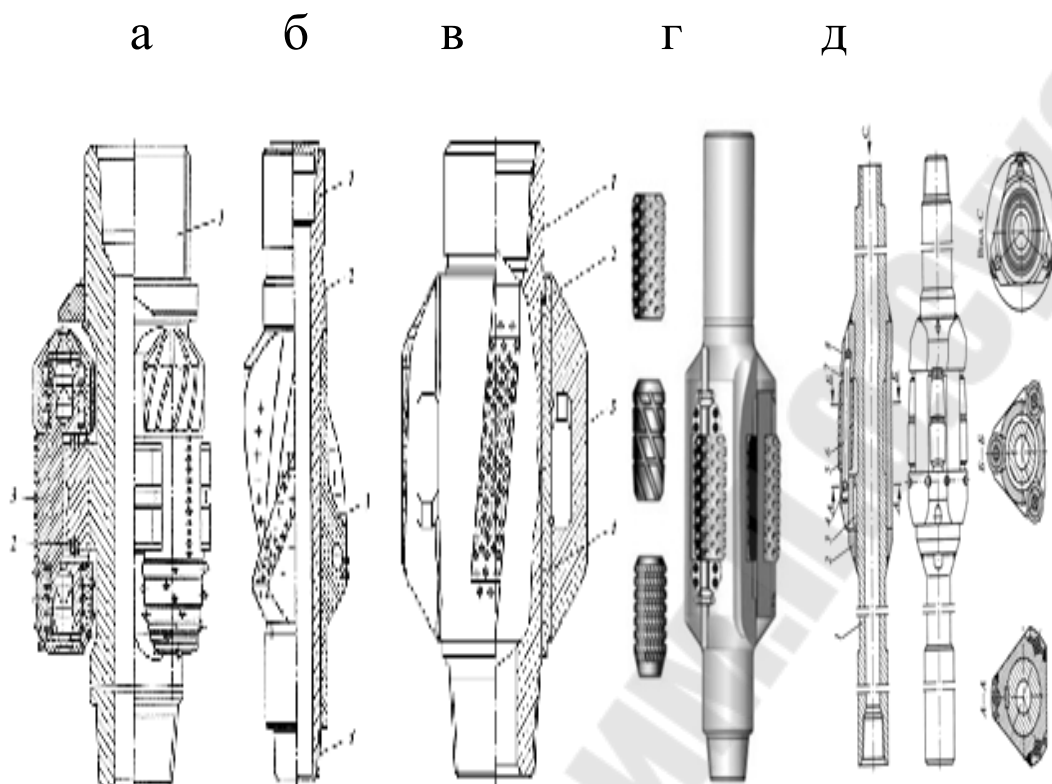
Конструкции опорно-центрирующих устройств: а – калибратор шарошечный типа КШУ; б – калибратор со сменными спиральными лопастями типа 8 КС; в – калибратор – центратор с прямыми лопастями типа КЦЛ; г, д – стабилизатор со сменными шарошками
